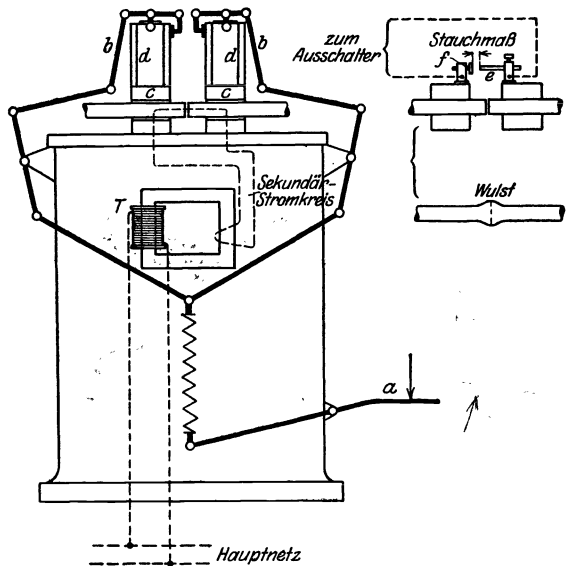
Schema einer Stumpfschweißmaschine.
